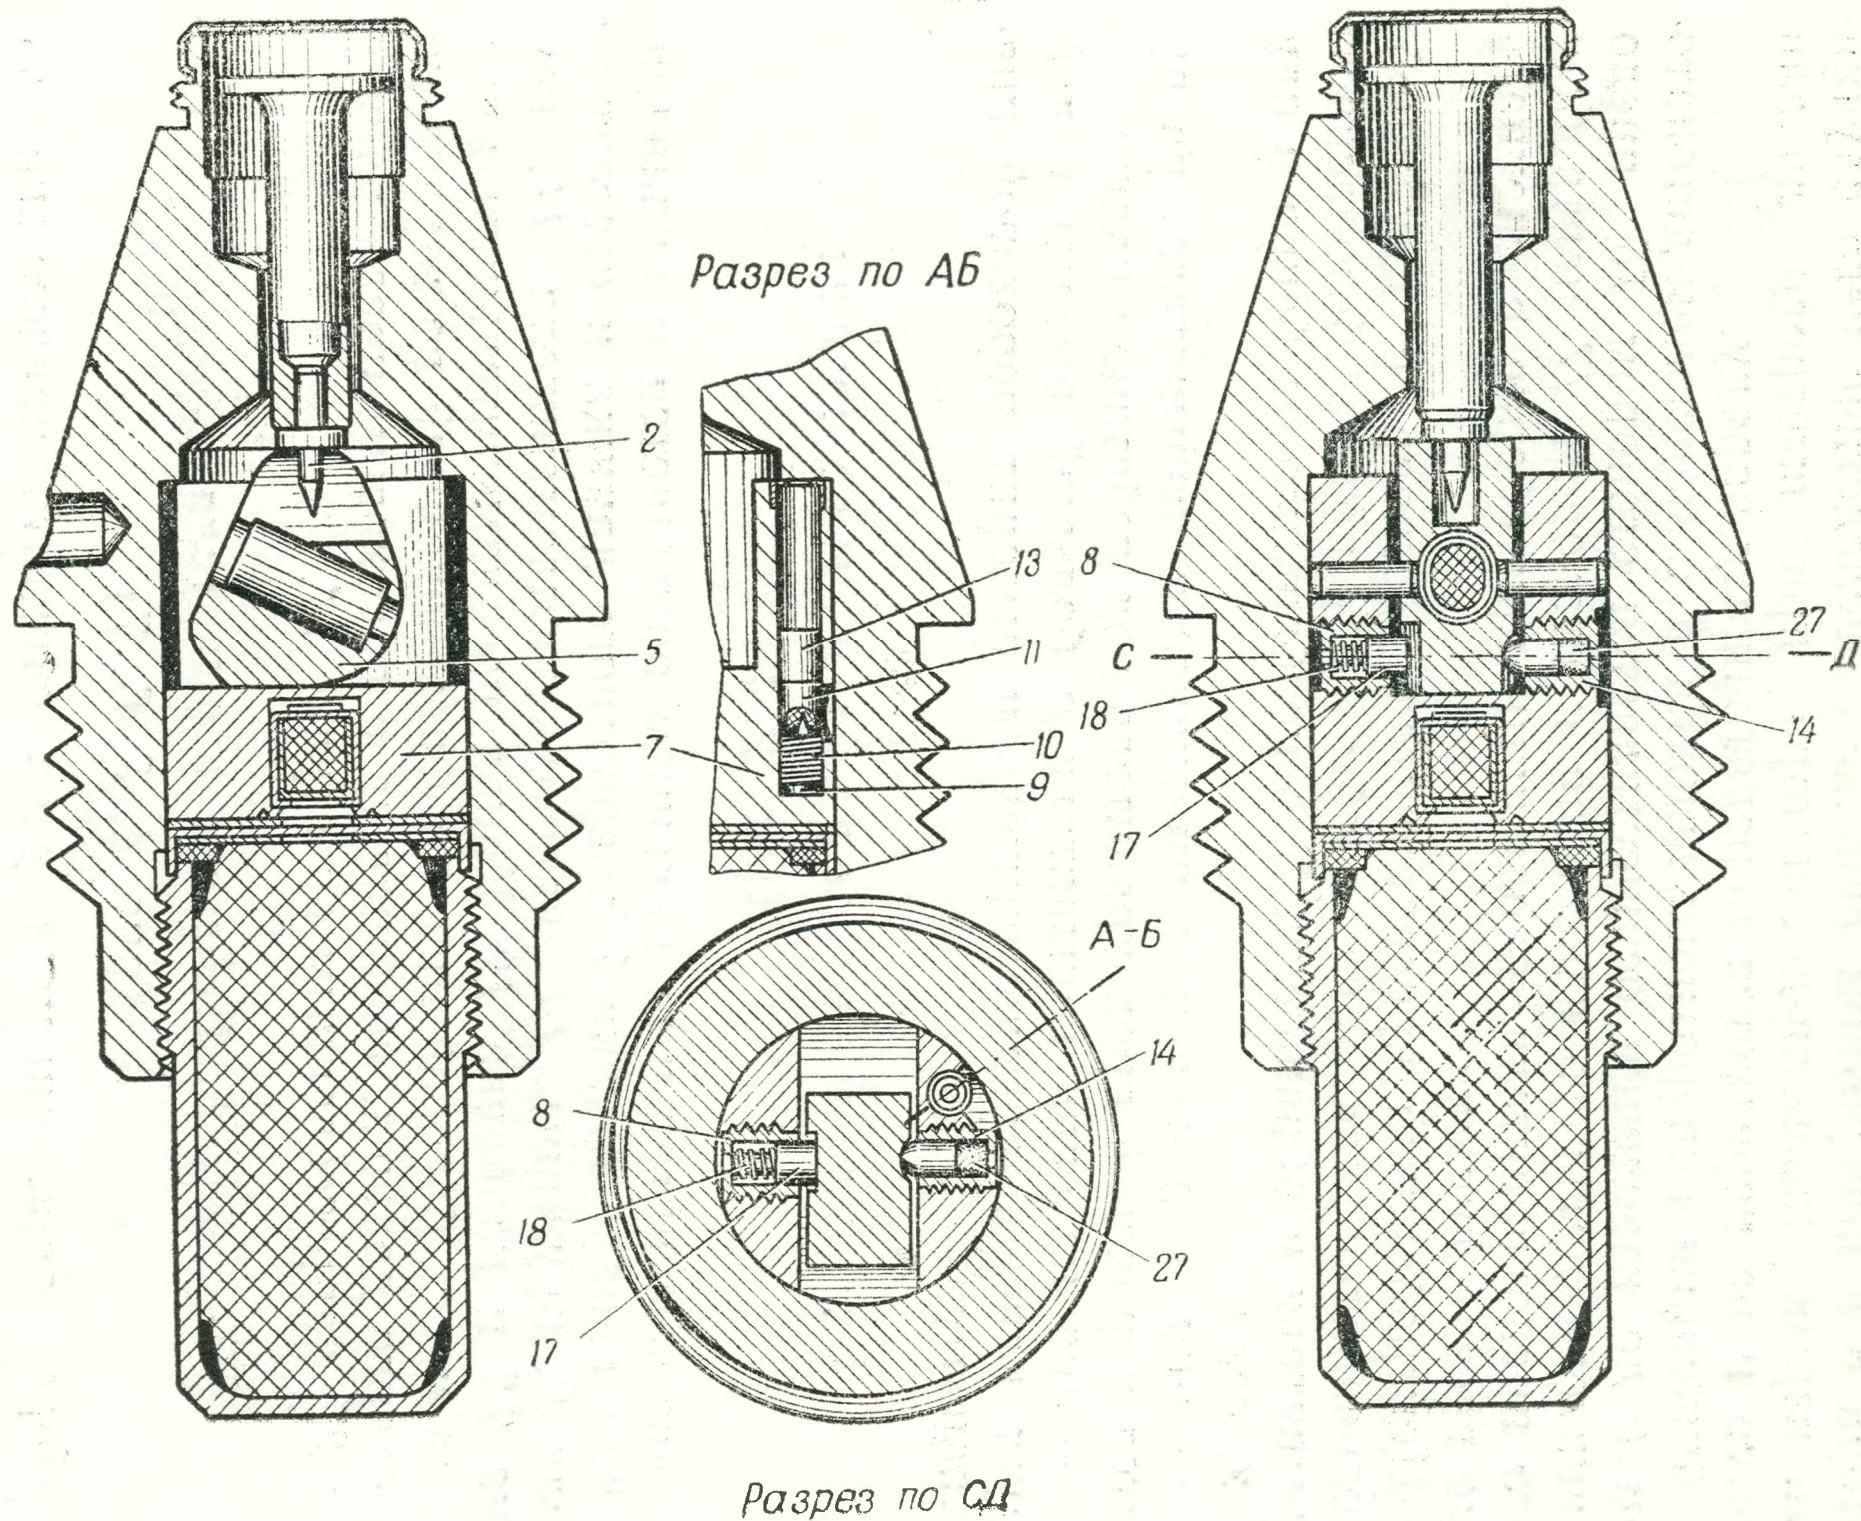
Положение деталей взрывателя при вылете снаряда из канала ствола орудия: 1 — ударный стержень; 4 — мембрана; 5 — поворотный движок; 16 — стопор; 17 — стопор
